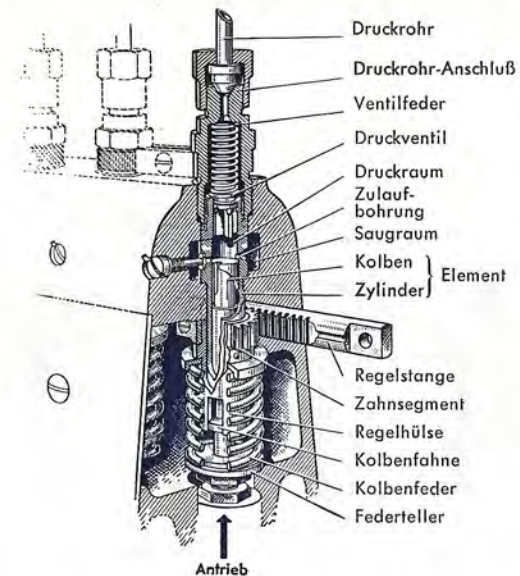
Pumpenelement einer PE..B-Pumpe im Schnitt
